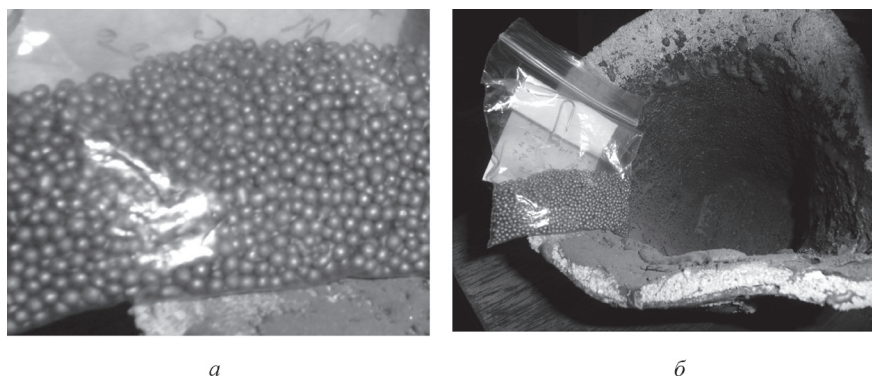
Внешний вид дроби с покрытием (а), разливочный ковш (б)
